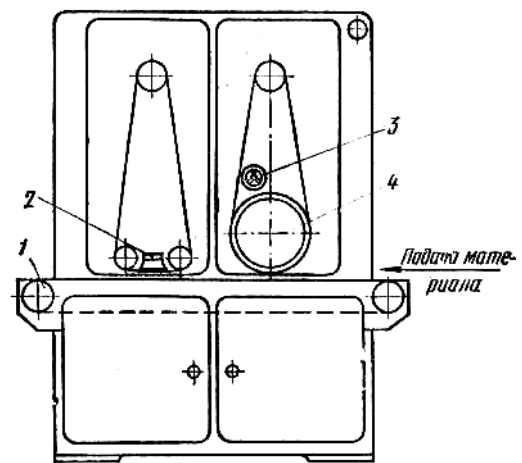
Шлифовальный широколенточный станок с верхним расположением агрегатов: 1 — конвейер, 2, 4 — шлифовальные агрегаты, 3 — маховичок настройки на толщину сошлифовываемого слоя
